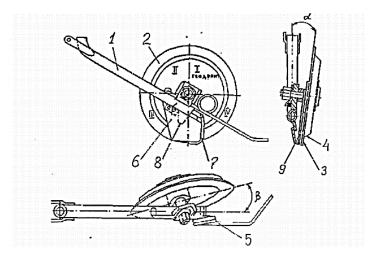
Однодисковый сошник тарельчатой формы: 1 – корпусная труба; 2 – тарельчатый диск; 3 – плоская поверхность диска; 4 – опорная поверхность диска; 5 – загортач; 6 – киль; 7 – клапан; 8 – выходное отверстие семянаправителя; 9 – направляющая пластина
